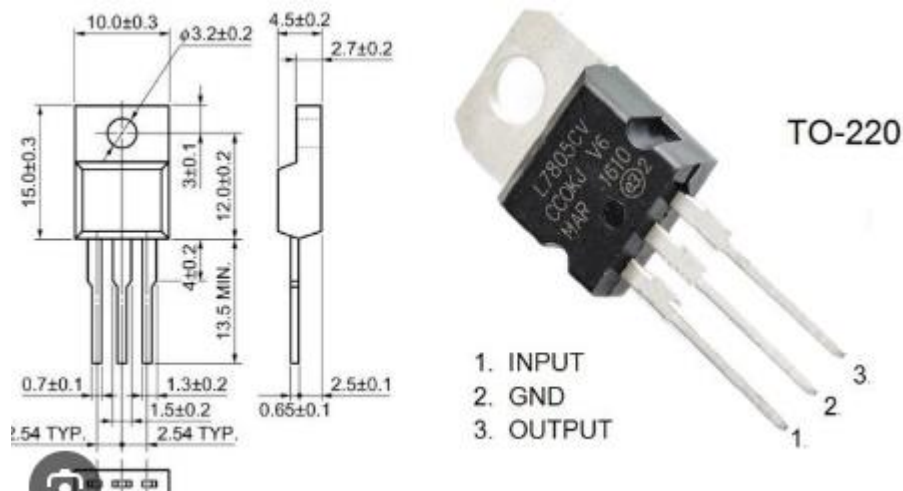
Габаритні розміри стабілізатора L7805
